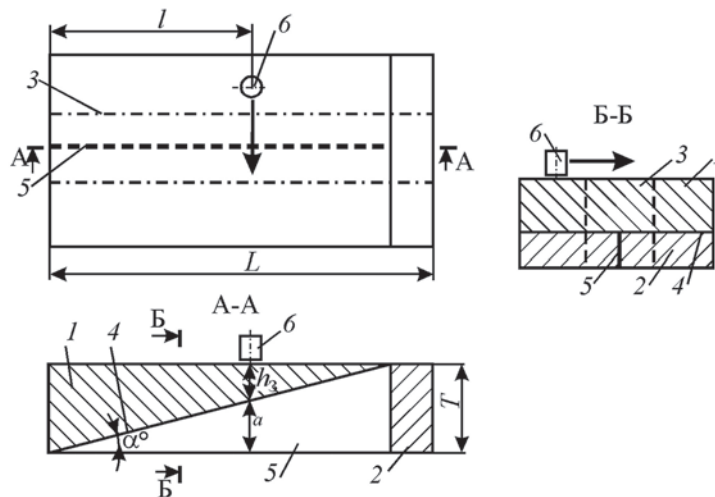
Складений багатозначний СЗ для імітації поверхневих і підповерхневих дефектів у плоских ОК зі зварним швом: 1, 2 – клиновидні частини; 3 – область зварного шва; 4 – стик; 5 – ШД дефект; 6 – ВСП
